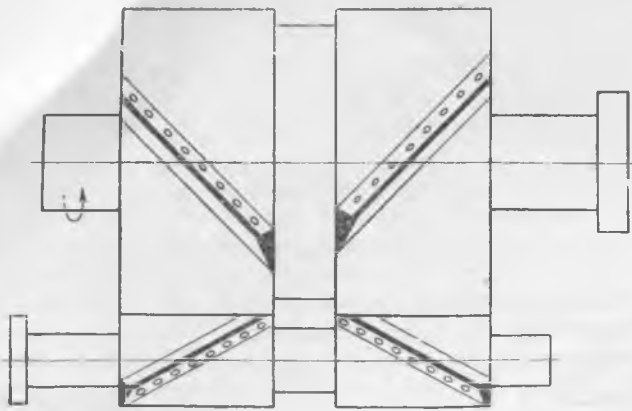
Перенасадка зубчатых венцов колеса и поворот их на 180° на своей же ступице.
